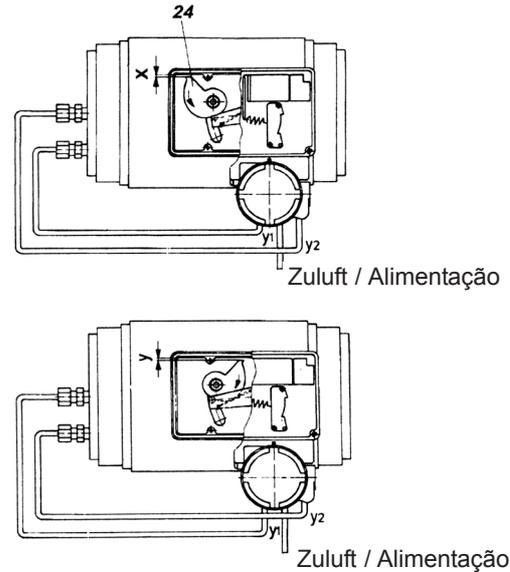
Atuador rotativo com conjunto de montagem para movimento rotativo e posicionador de dupla ação.
